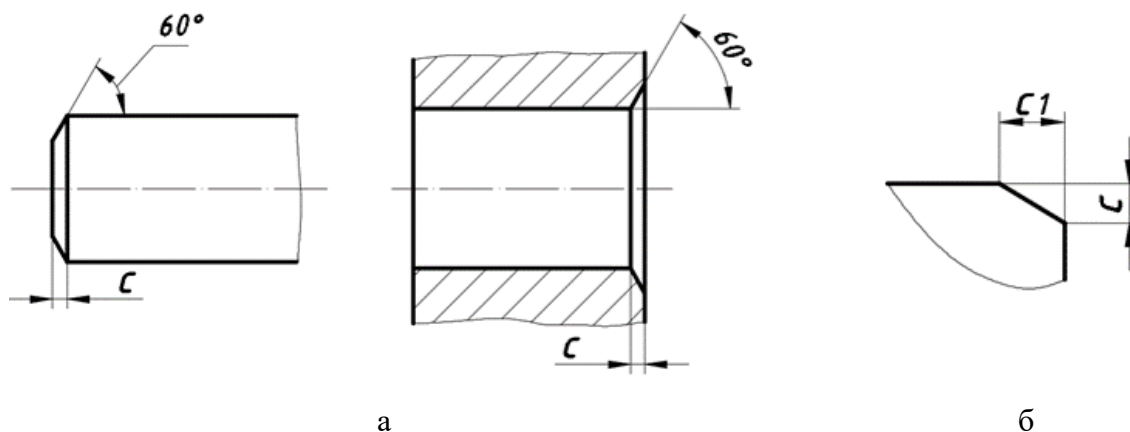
Образец выполнения фаски под углами отличными от угла 45°.
